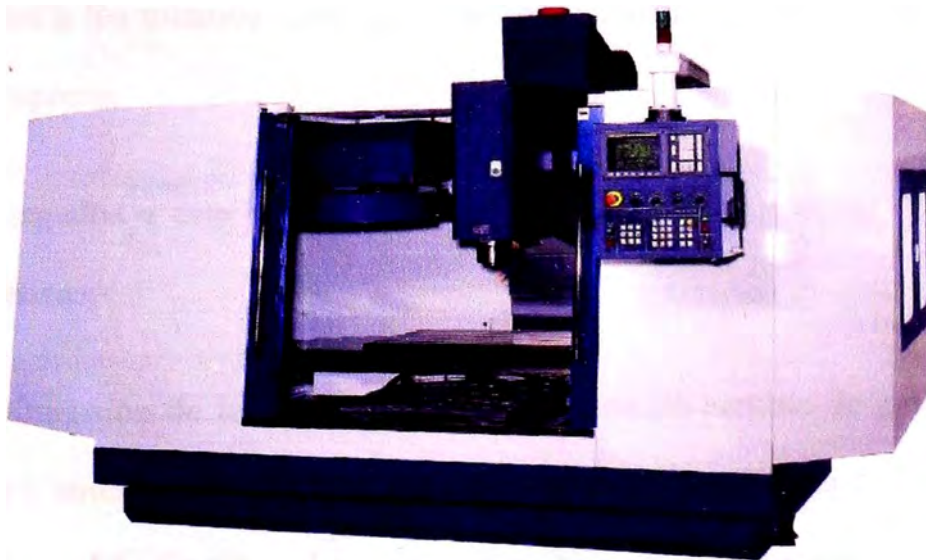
Centro de mecanizado: vertical para fabricantes de moldes.
